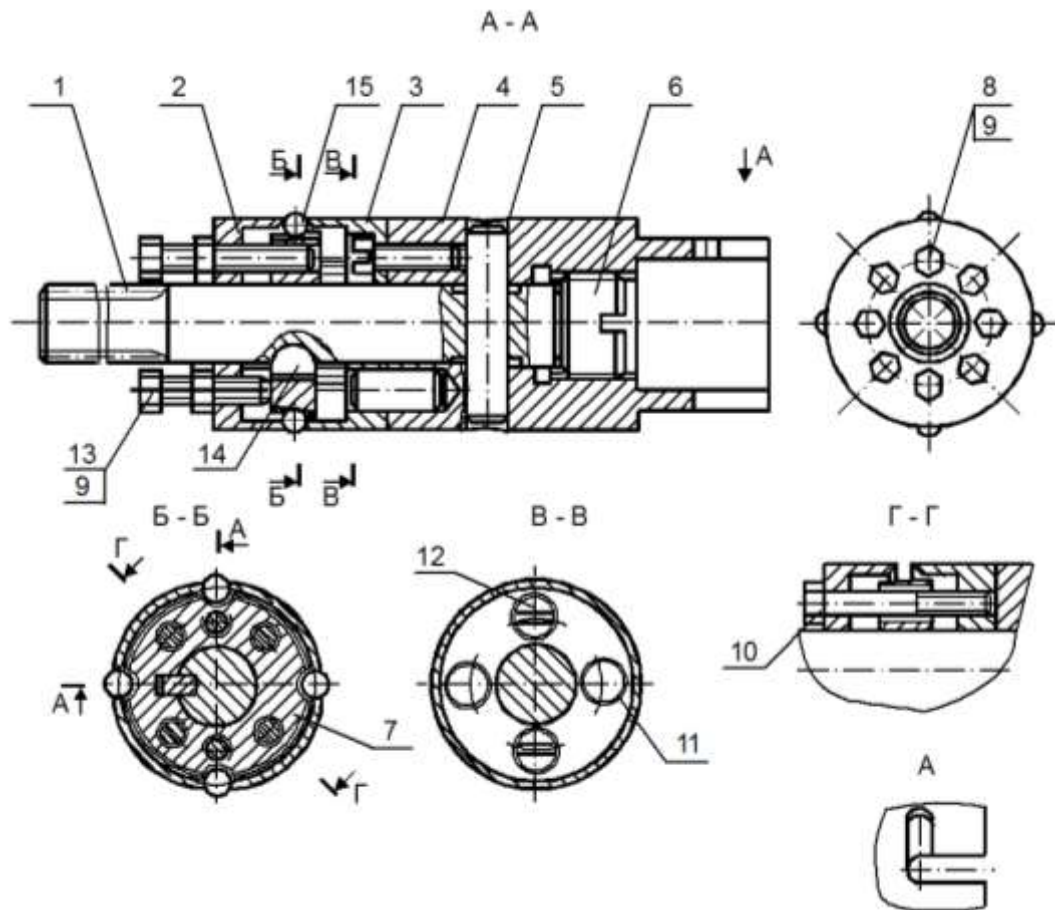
Конструкція багатокулькового розкотника: 1 – вал шліцьовий; 2 – кільце сепаратора рухоме; 3 – кільце сепаратора нерухоме; 4 – корпус; 5 – палець; 6 – пробка різьбова; 7 – конус; 8, 10, 13 – болт регулюючий; 9 – контргайка; 11 – штифт установочний; 12 – гвинт; 14 – шпонка; 15 – елемент деформуючий (кулька).
